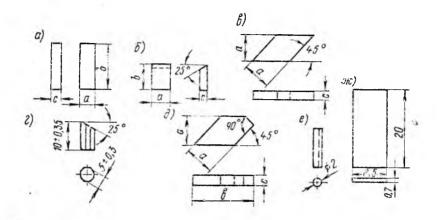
Формы твердоспланных резцов: а - призматическия; б - пластинчатая; в, д - косоугольная; г - восьмигранная; е - цилиндрическая; ж - тонкопластинчатая
